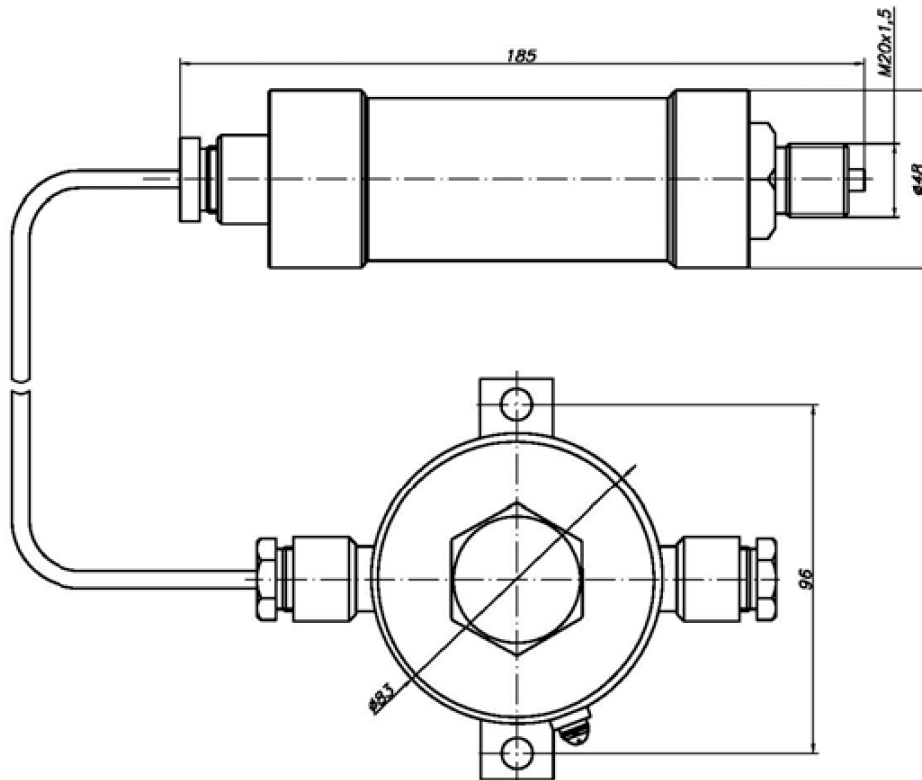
Габаритный чертеж датчиков избыточного давления Дон 17 моделей 11X5
